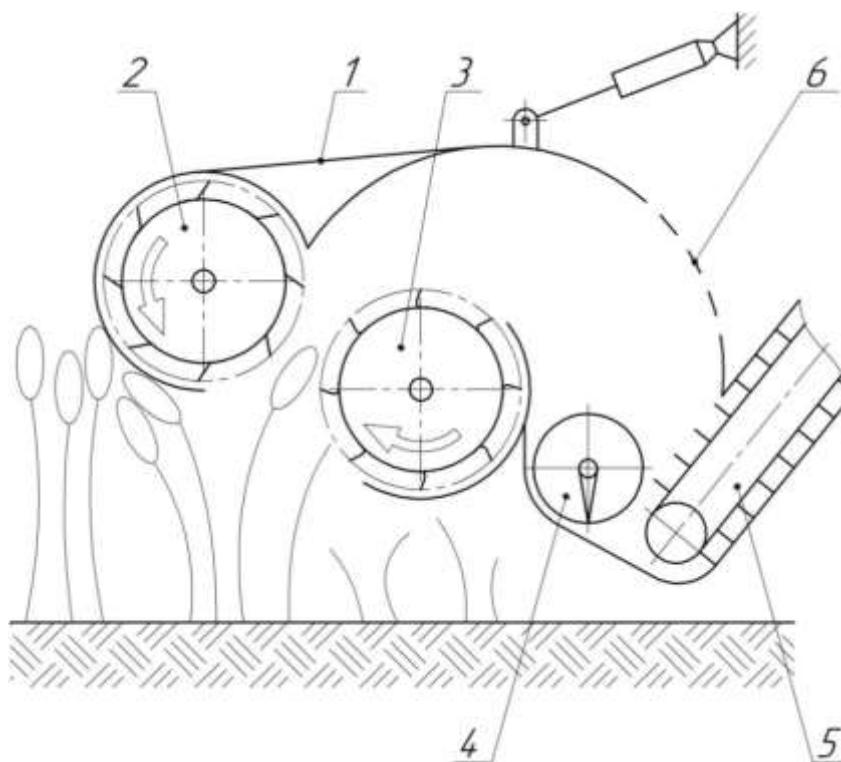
Устройство для обмолота сельскохозяйственных культур на корню (SU авторское свидетельство № 1165278): 1 – корпус; 2 – подающий барабан; 3 – очесывающий барабан; 4 – шнек; 5 – плавающий транспортер; 6 – сетчатая поверхность
